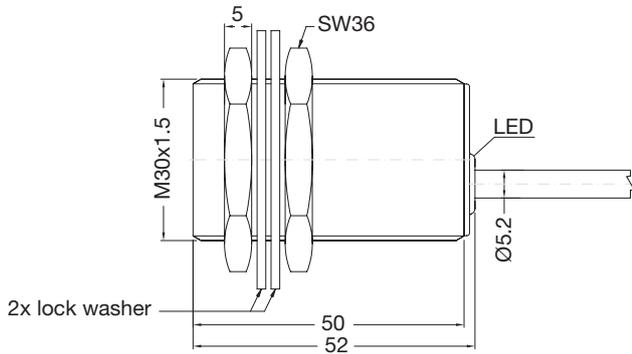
Lange Ausführung, bündiger Einbau, Kabel
